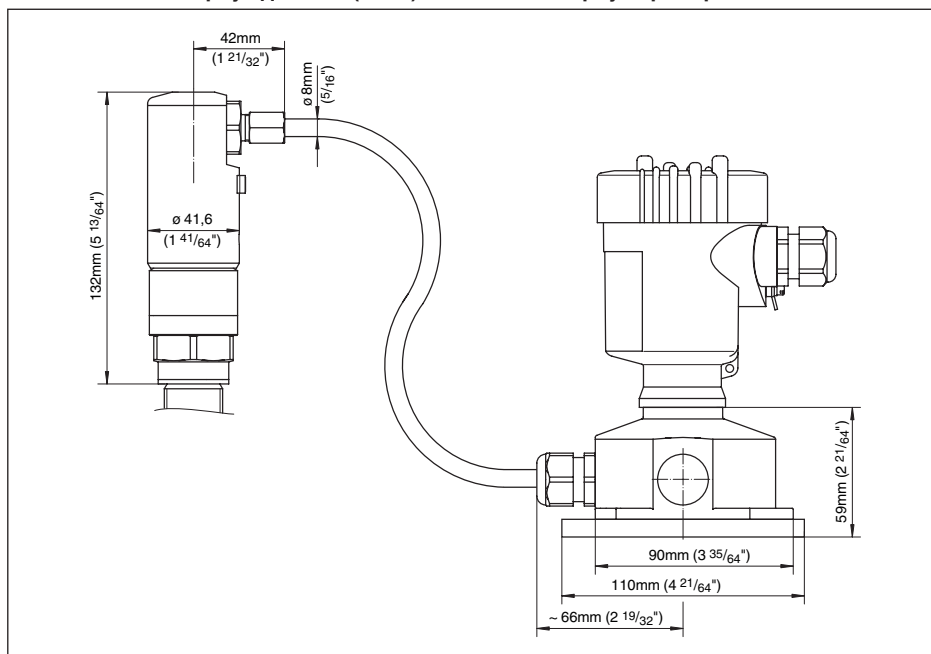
Металлический корпус датчика (IP 68) (10 bar) и выносной корпус прибора
